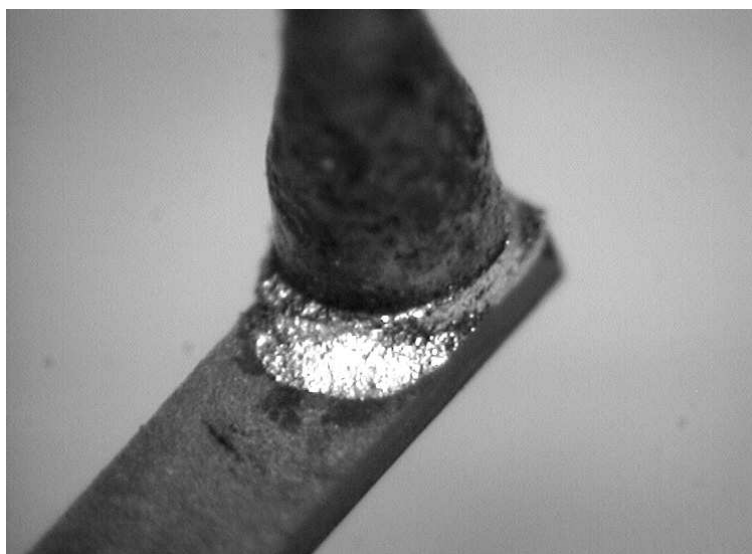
Collage de la pointe par de la laque d'argent électriquement conductrice.
